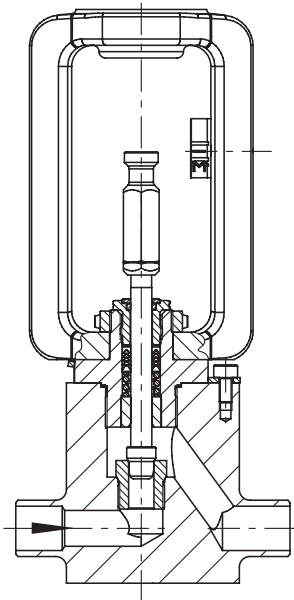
Válvula para altas presiones Tipo 3252 de paso recto con extremos para soldar
